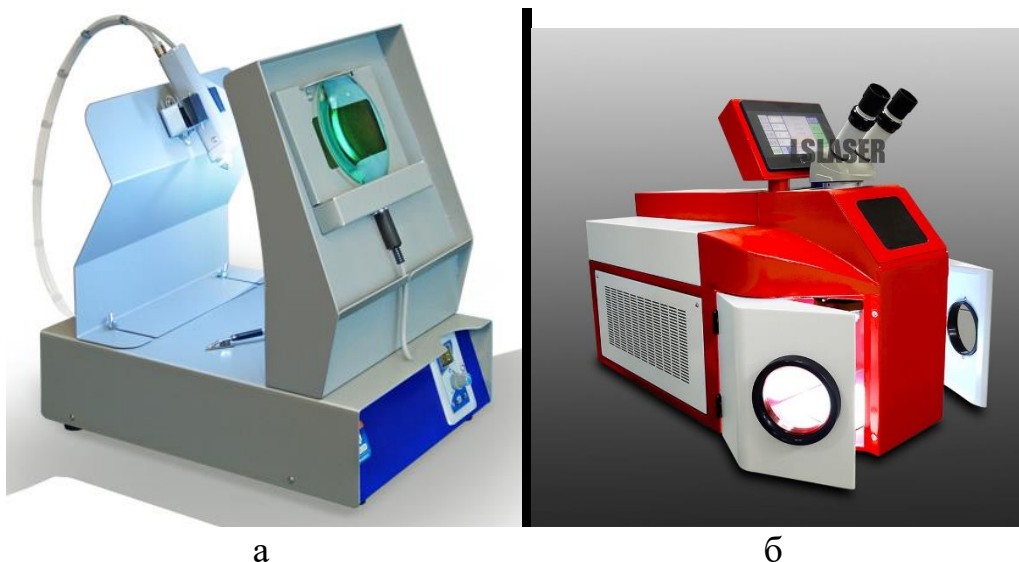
а) Сварочный аппарат Молния-2 (Россия); б) сварочный аппарат Desktop (Китай)
